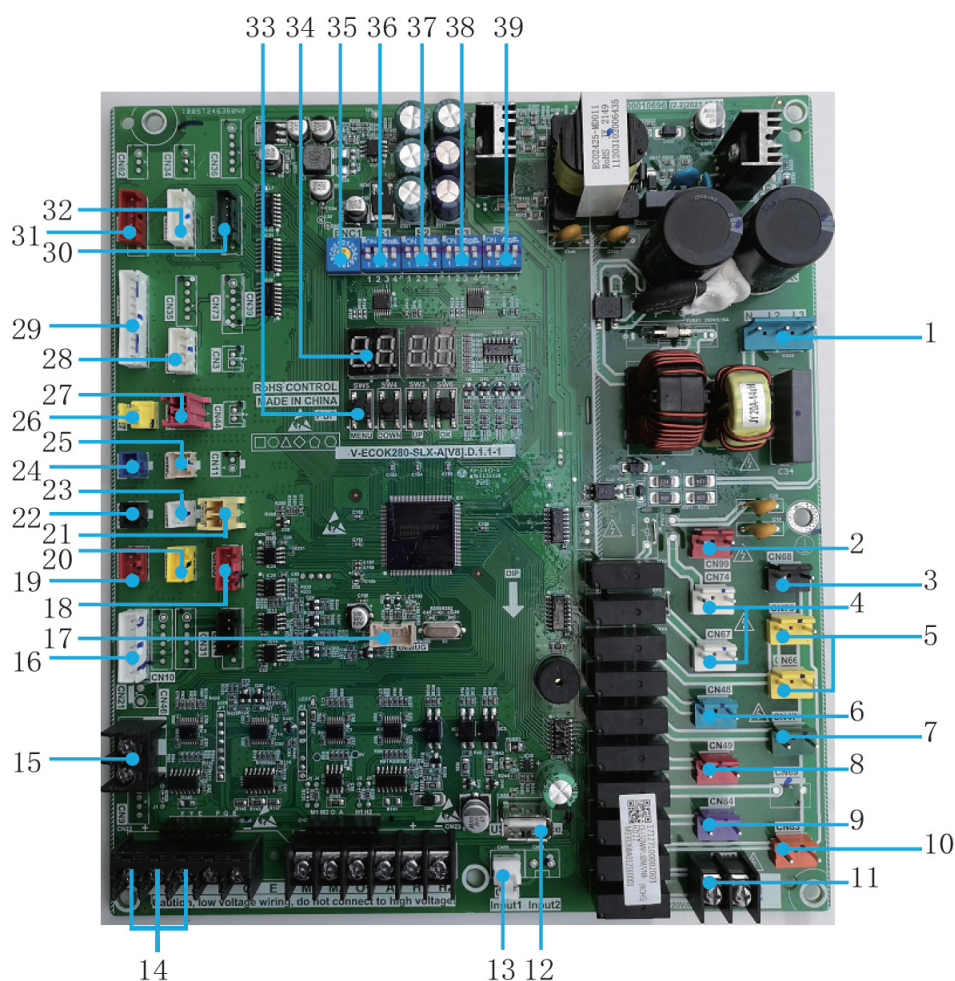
Placa principal do KEM-75 DRS5 KH e KEM-140 DRS5 KH
